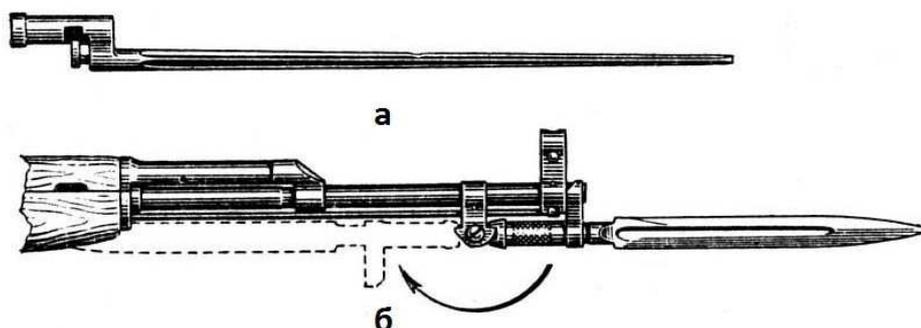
Общий вид двух конструктивных решений крепления штыков:
